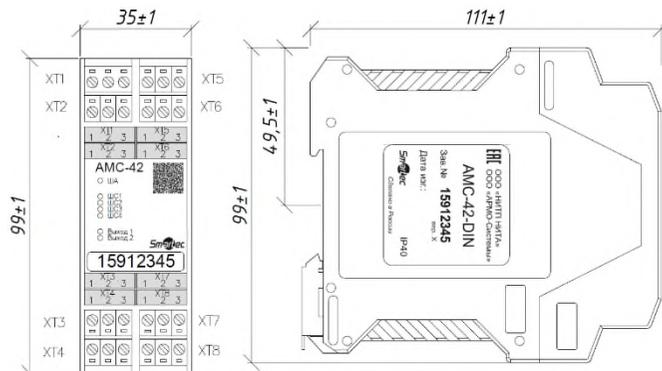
Размеры и внешний вид модуля исполнения AMC-42-DIN.
